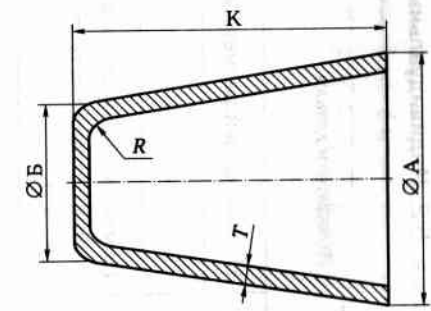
Чертеж детали, получаемой глубокой вытяжкой
